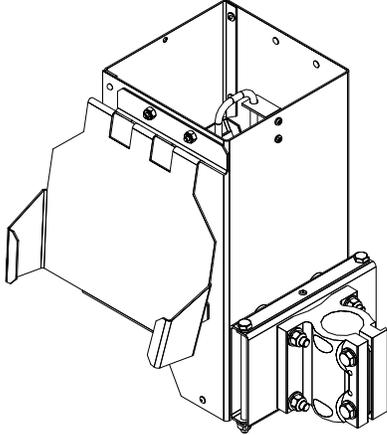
MONTAJE DE TUBO HORIZONTAL
